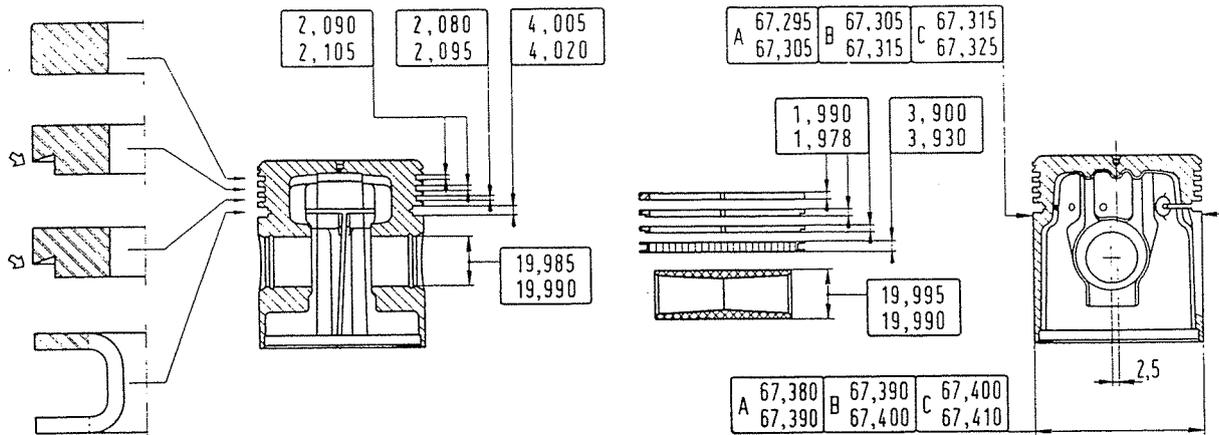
Hauptabmessungen der Kolben, Kolbenbolzen und Kolbenringe.
